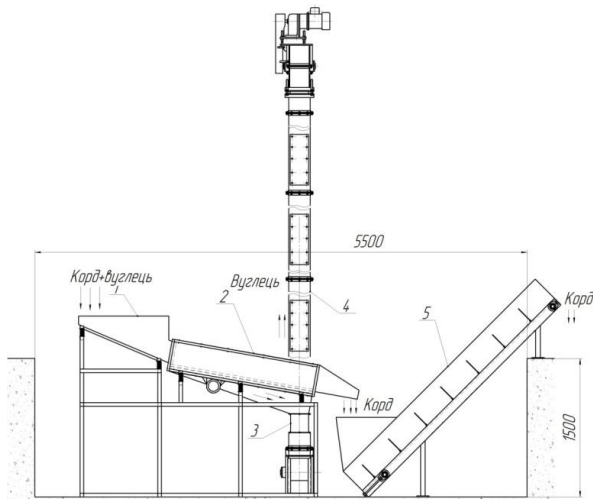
Технологічна схема для механічної очистки технічного вуглецю
